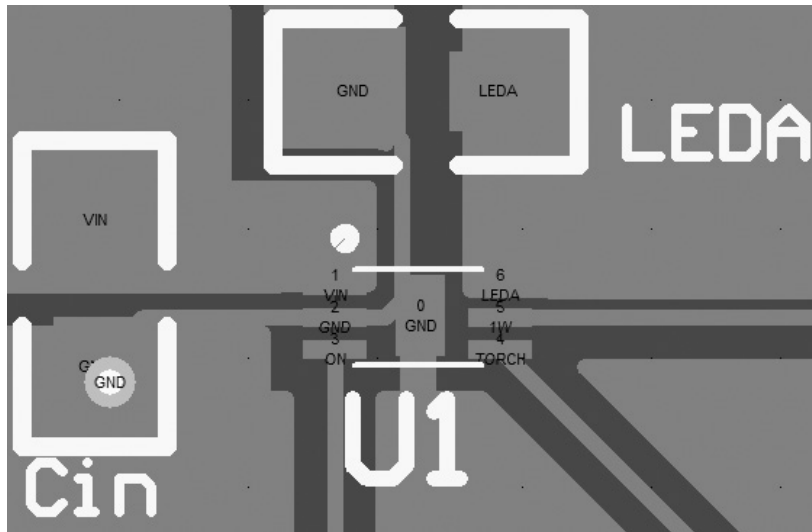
UTDFN-1.5x2-6L 的 PCB 布线图
